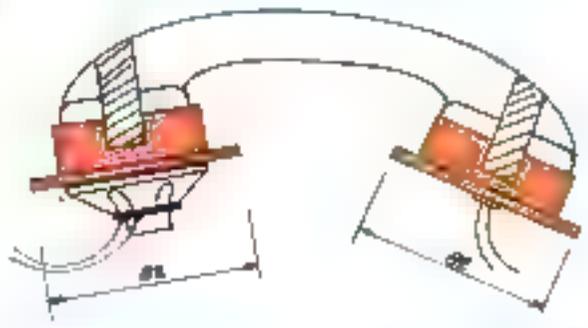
Montage de la carte PCB. Les pièces sont à assembler en double exemplaire de chaque côté de la carte à trois plans.
